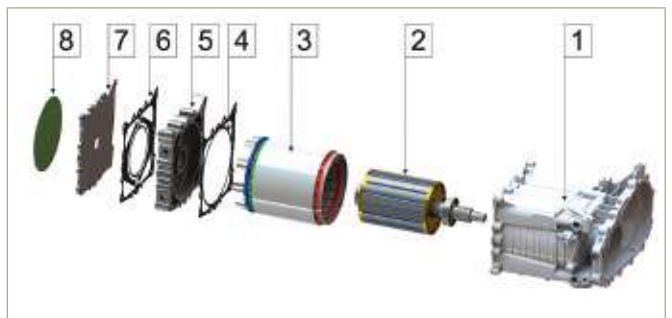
Explosionszeichnung des IPM-Antriebs
